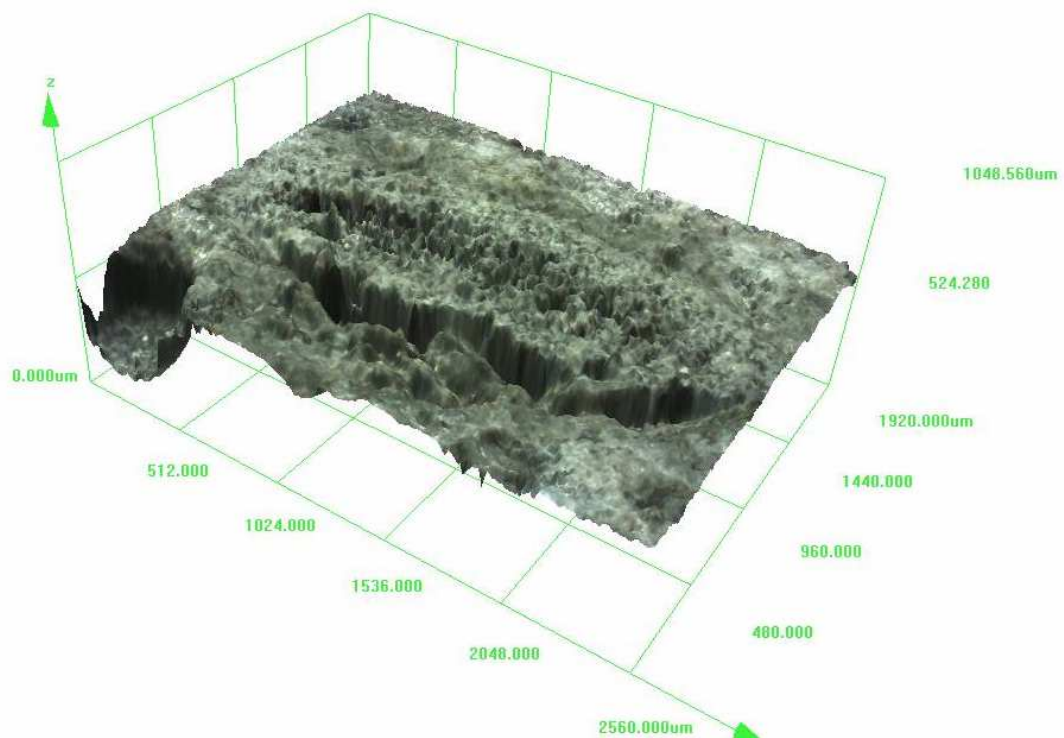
3D zobrazení povrchu vzorku 1 – izoplochy souřadnice Z
